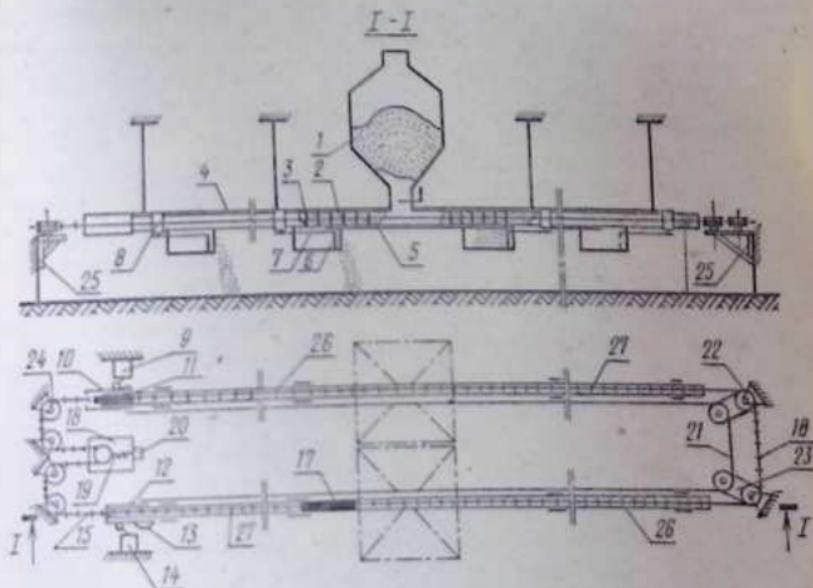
Схема автоматического кормораздатчика РКА-1000:
